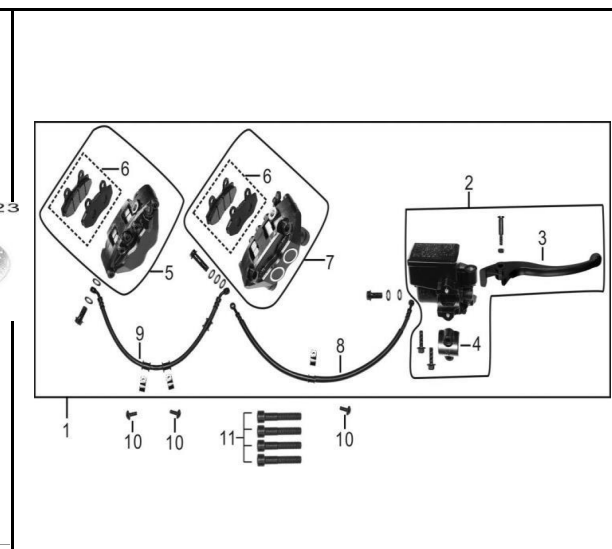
CALIPERS Y BOMBA DE FRENO DELANTERO
